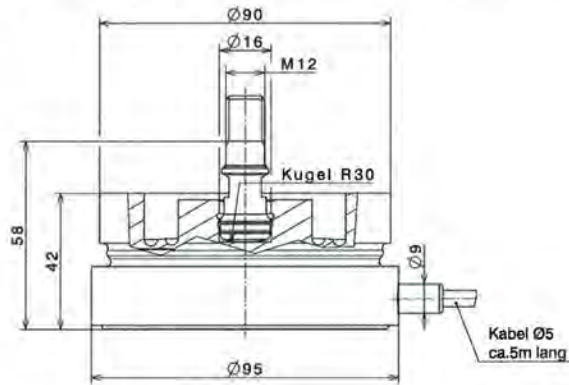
Abmessungen der Wägezelle Typ PR 6261 / Figure 2: Dimensions of the load cell type PR 6261
